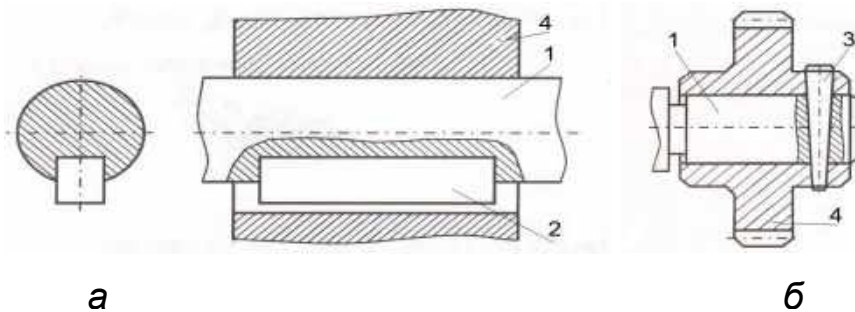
Приклади типових з'єднань зубчастих коліс із приводним валом: а – шпонкове, що допускає осьове переміщення; б – штифтове нерухоме (1 – вал; 2 – шпонка; 3 – конічний штифт; 4 – зубчасте колесо)
